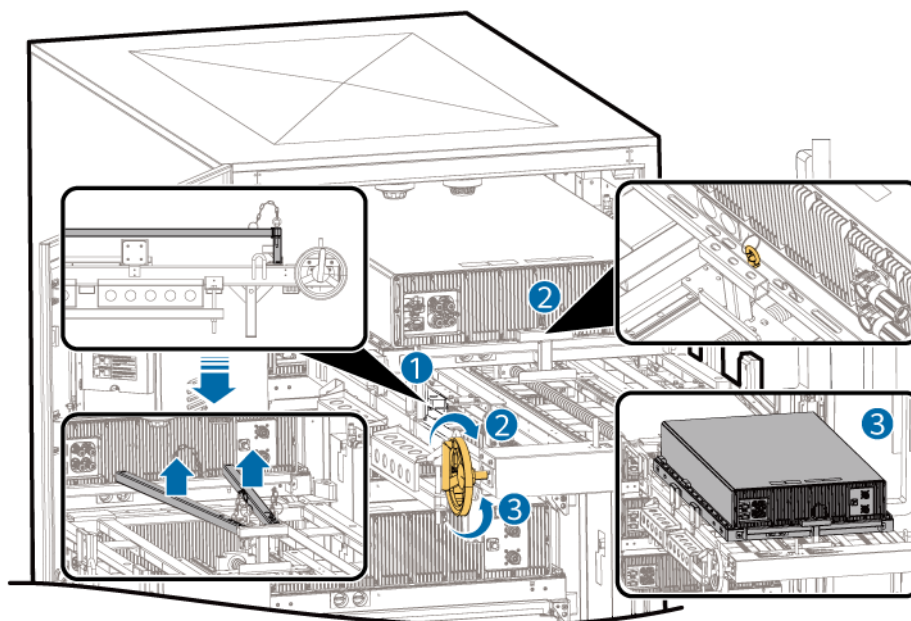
Regolazione della posizione del dispositivo di fissaggio
